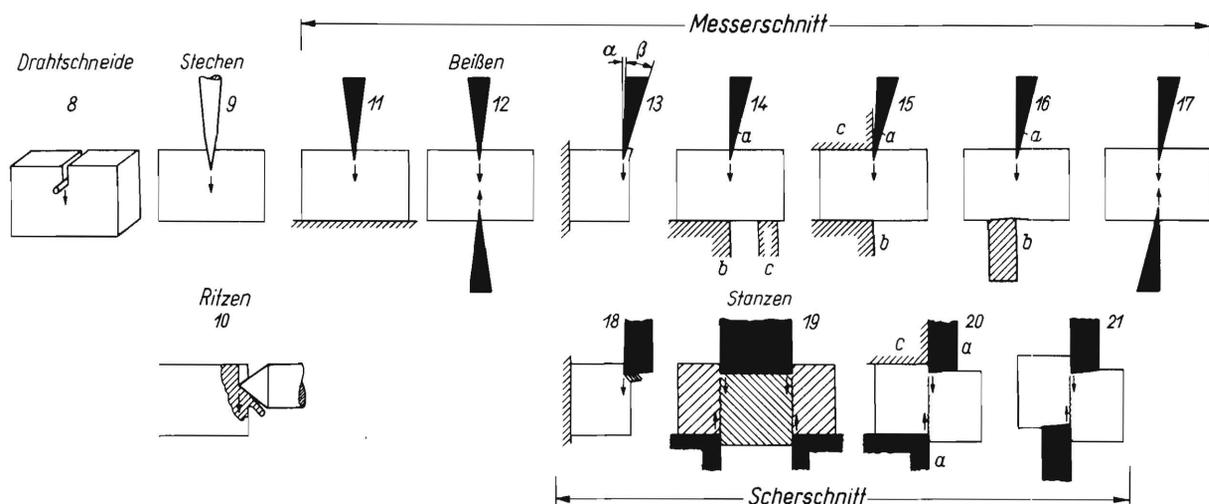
bis 21. Grundformen der Schneidwerkzeuge (schematisch). Die Pfeile geben die Schnittrichtung an.
